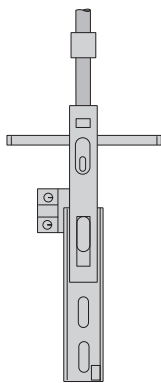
L-Antrieb für Beton- bzw. Stahlmast
